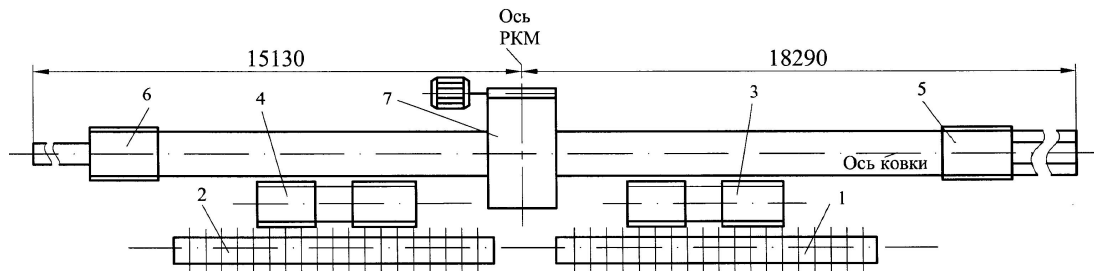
Ковочный комплекс, поставляемый фирмой GFM
